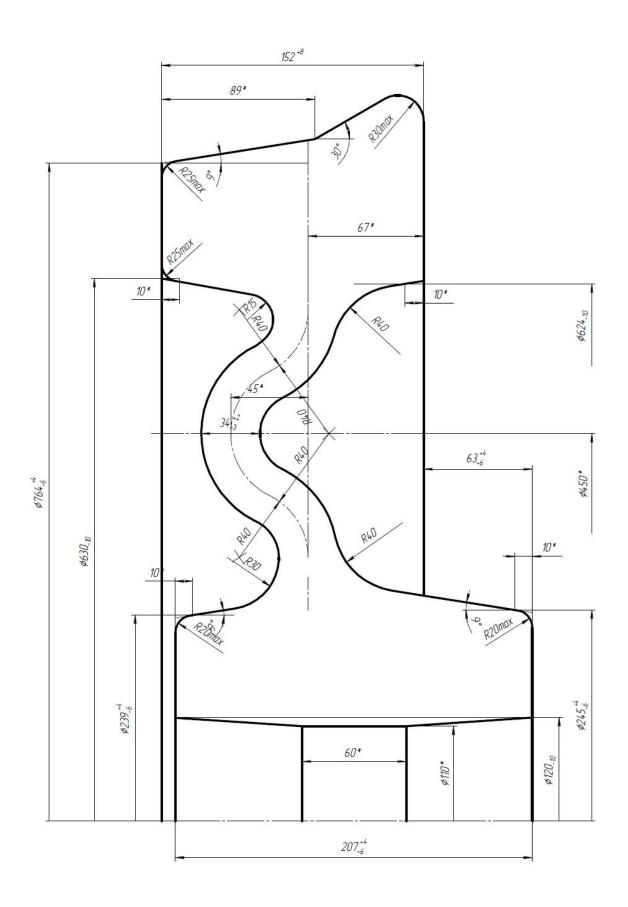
Колесо черновое Ø 764 мм по(д Ø 750 мм черт. № 29240,ред. Е). Масса чернового колеса, рассчитанная на  $^2/_3$  поля допуска = 394 кг.
